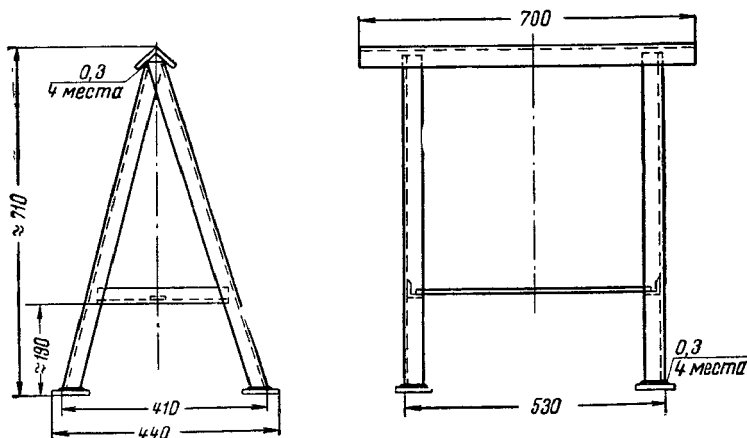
Козлы для разборки крышки трансформатора (размеры в мм).
